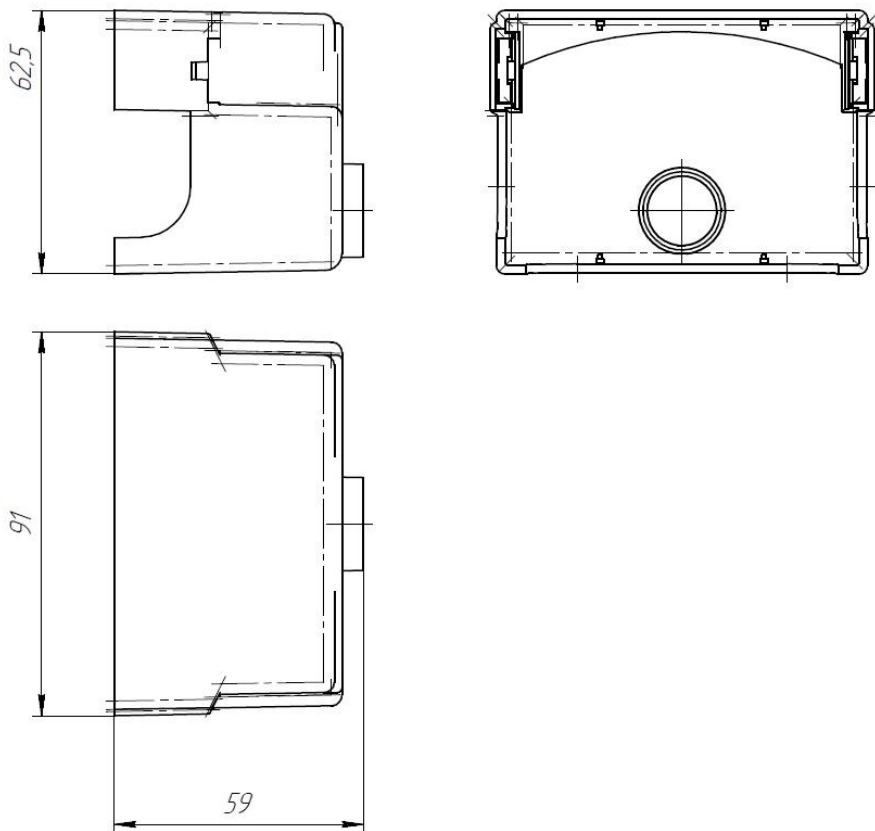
Конструкция и габаритные размеры автомата горения щитового исполнения.
